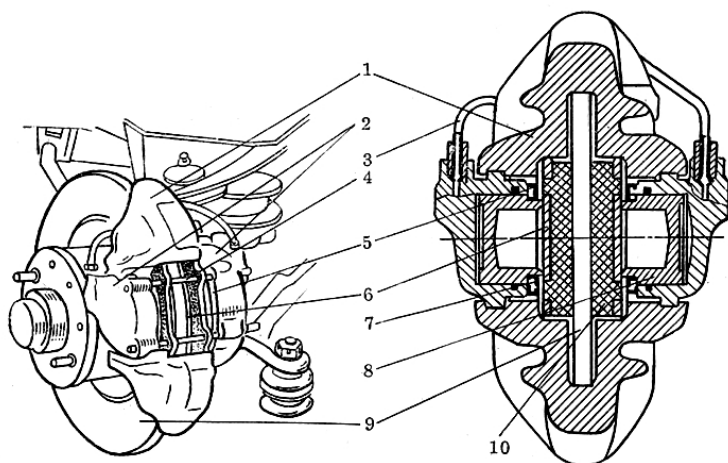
Дисковый тормозной механизм с неподвижным суппортом и сплошным диском: 1 — неподвижная скоба; 2 — колесные цилиндры; 3 — соединительная трубка; 4 — направляющие штифты; 5 — пылезащитный чехол; 6 — колодки; 7 — уплотнительное кольцо; 8 — поршень; 9 — диск; 10 — накладки
